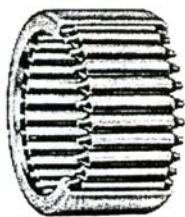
แสดง Needle Roller bearing แบบต่างๆ แบริ่งแบบนี้จะรับภาระได้สูงสุดในบรรดา Rolling-Element Bearings
